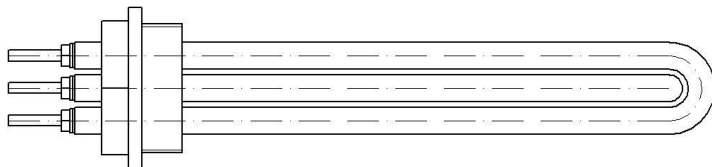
Трубчатый электронагреватель блочный ТЭНБ
